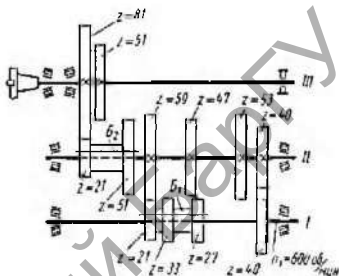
Коробка скоростей с передвижными блоками колес
